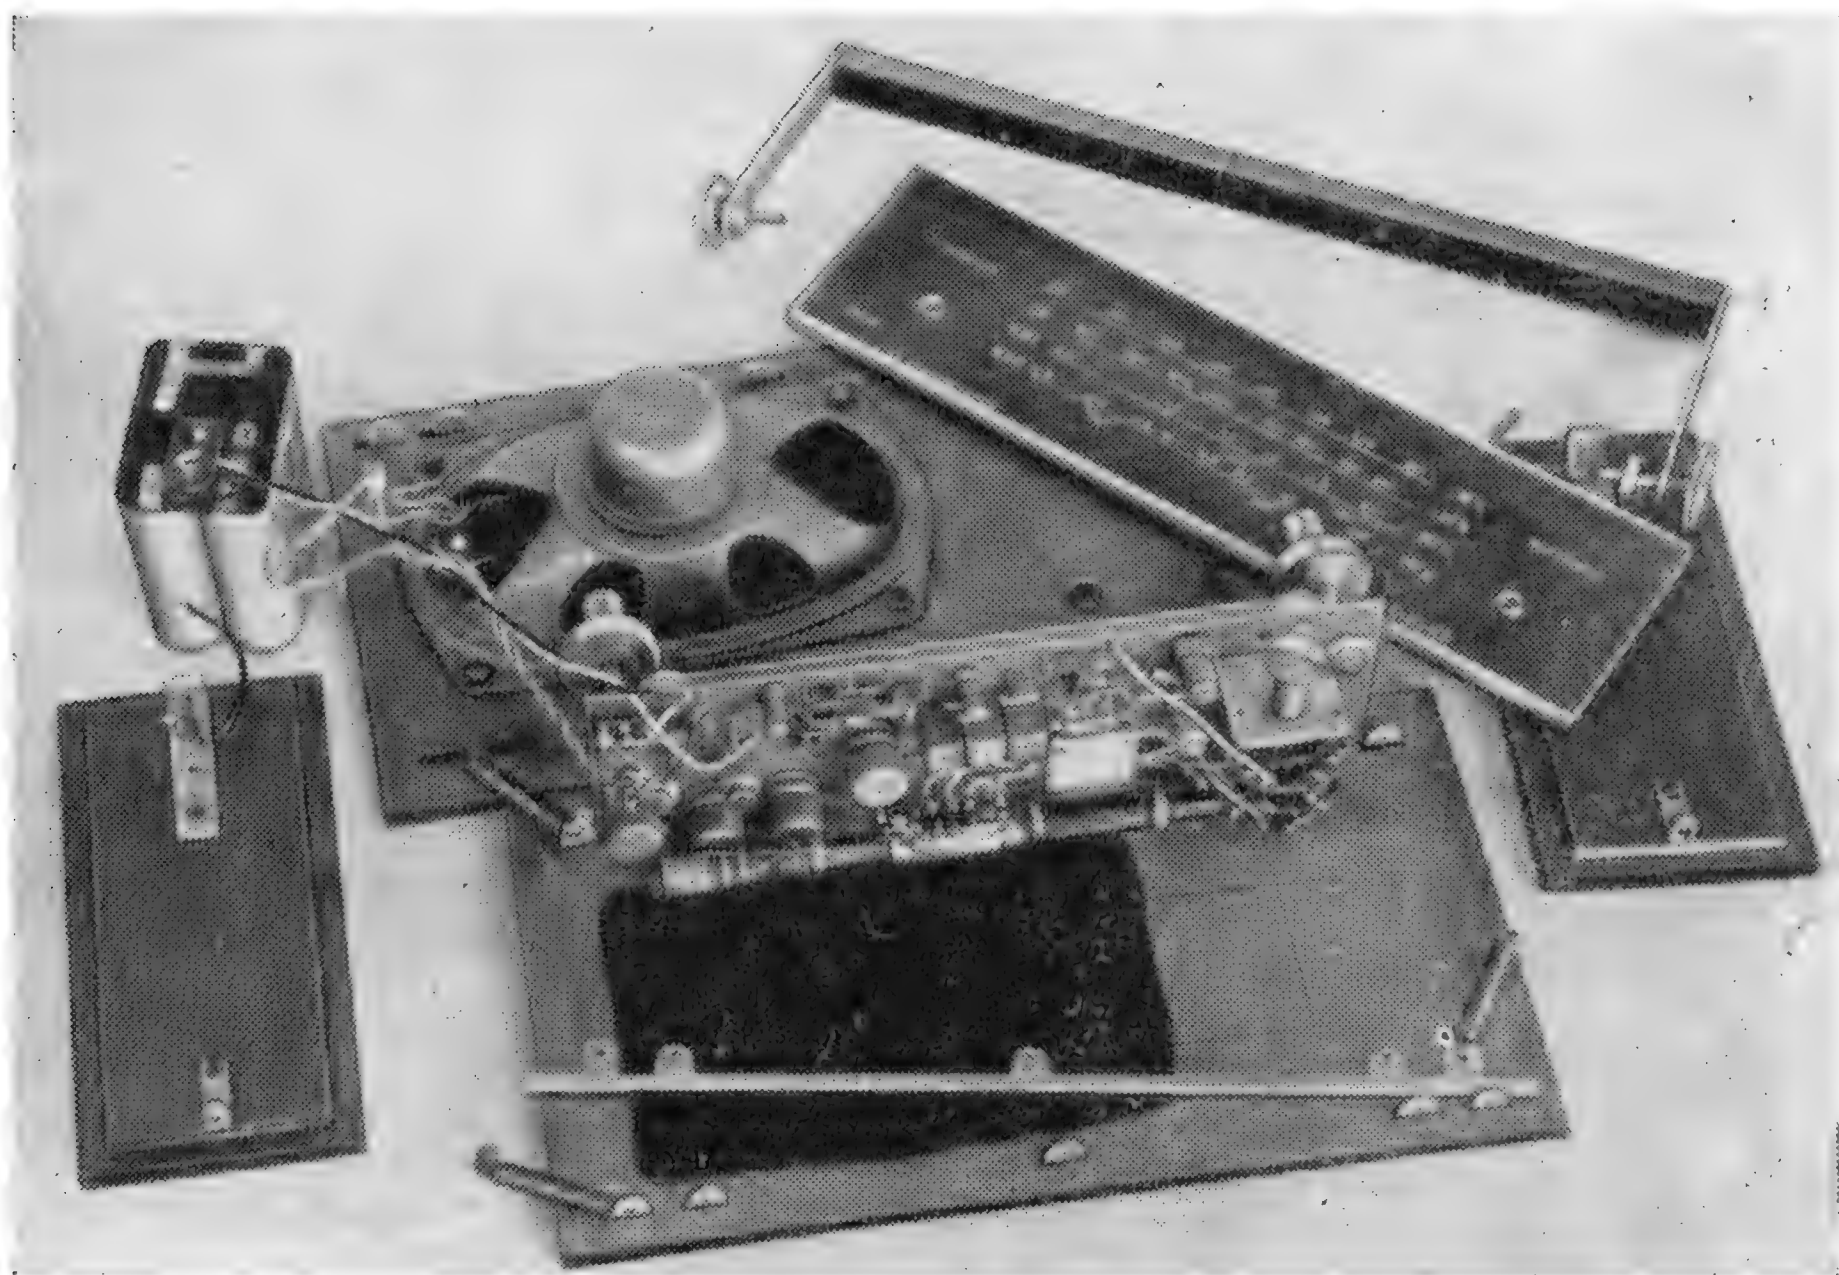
Конструкция корпуса и размещение деталей на нем.
